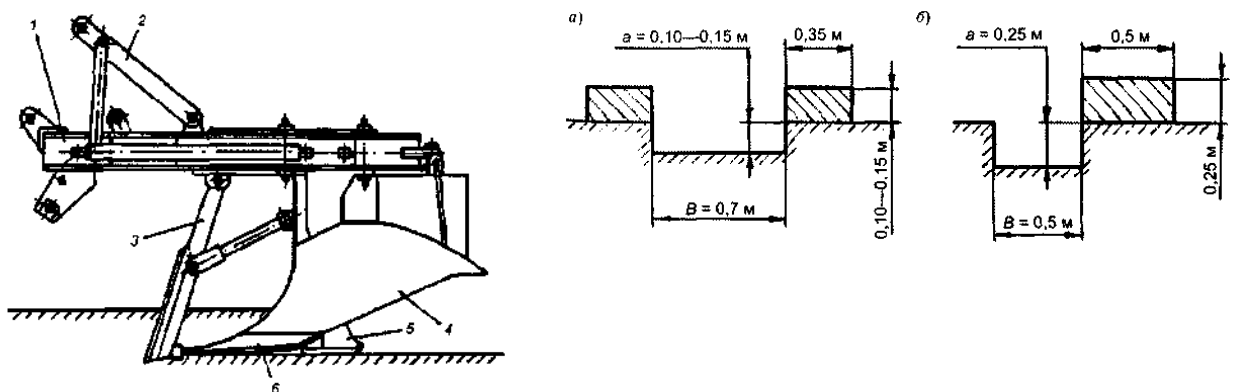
Лісовий плуг ПКЛ-70 для трьох операцій — оранки, висівання і садіння лісу; 1 — рама; 2 — начіпний пристрій; 3 — чересловий ніж; 4 — корпус двохолицевий; 5 — п'ята; 6 — леміш.
